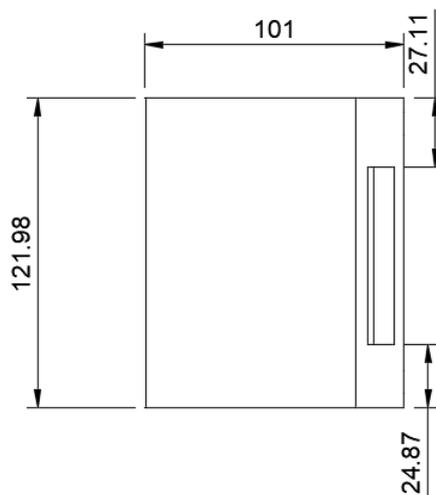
Medidas de la vista superior, parte superior del diseño en 3D
